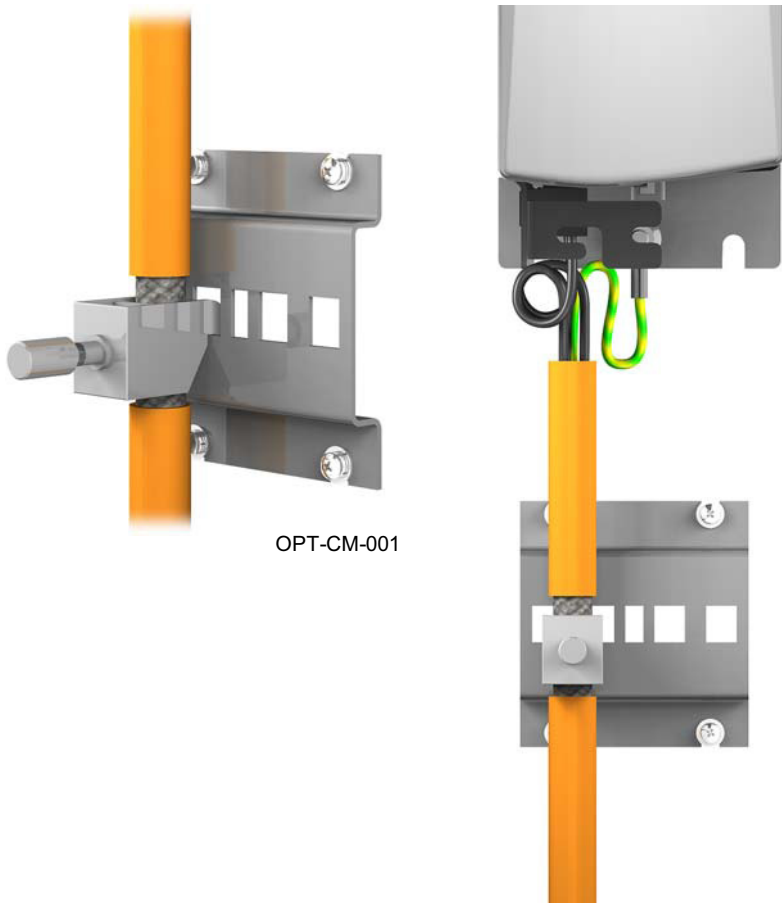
Halterung für die Kabelführung des Motorstromkabels
